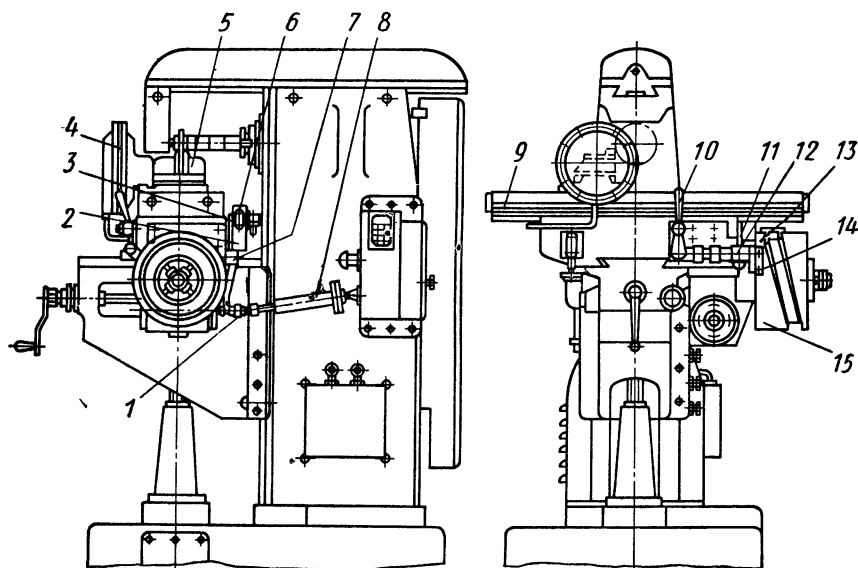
Автоматизация подачи стола фрезерного станка с помощью барабанного кулачка
